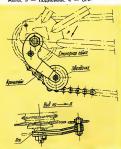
Устройство для регулировки натяжной цепи ножного привода.
